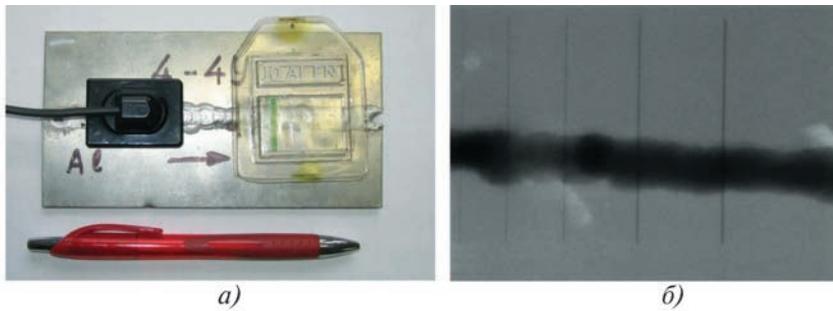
Рентгентелевизионный (а) сенсор S10811-11 на алюминиевом образце и изображение (б) сварного соединения (алюминий, толщина 2 мм) с использованием этого сенсора
